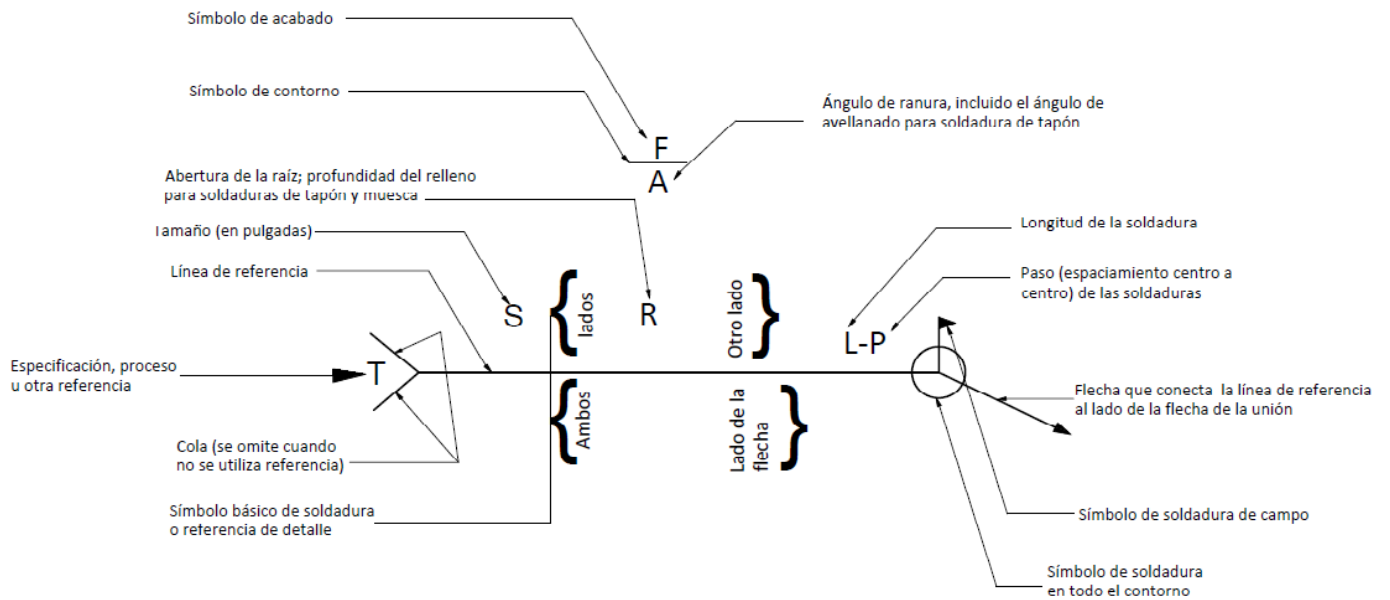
Símbolos para soldadura de taller y de campo
